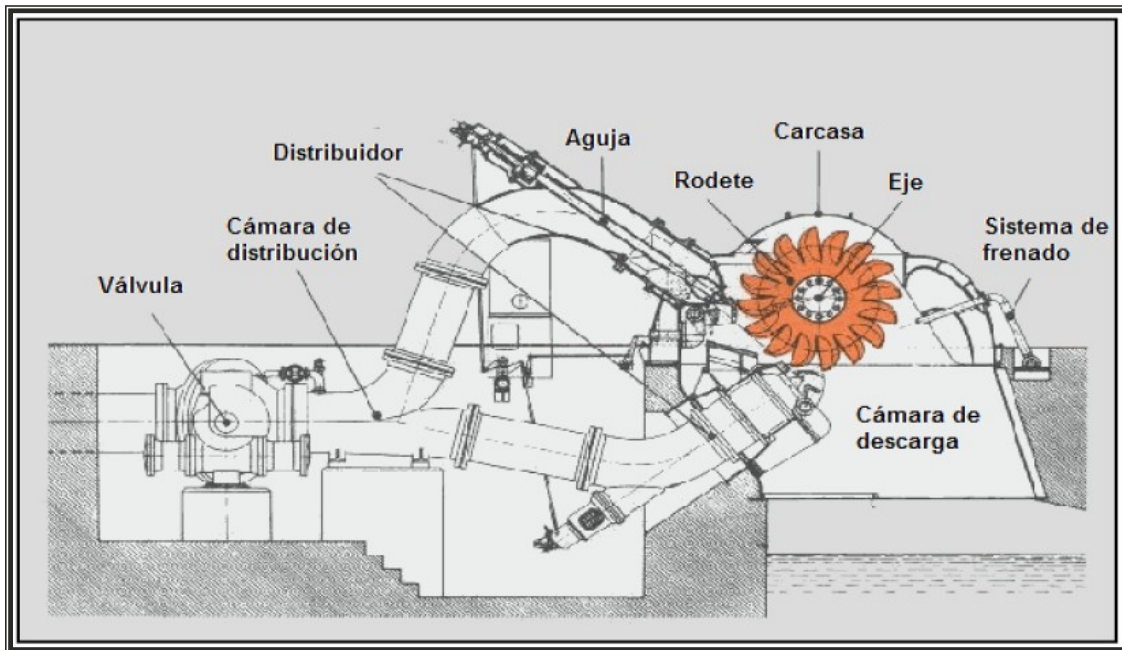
Componentes de una turbina Pelton de eje horizontal.
